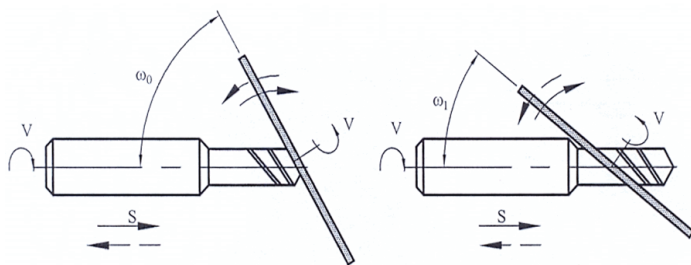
Схема изменения ориентации осей заготовки сверла и шлифовального круга методом поворота оси шлифовального шпинделя.
